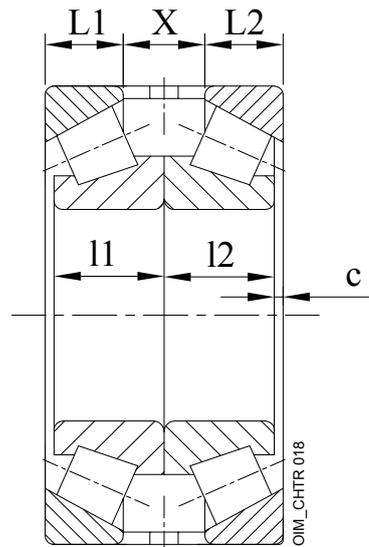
Отрегулировать упорный подшипник CHTR 4-5 (радиально-упорный шарикоподшипник)
